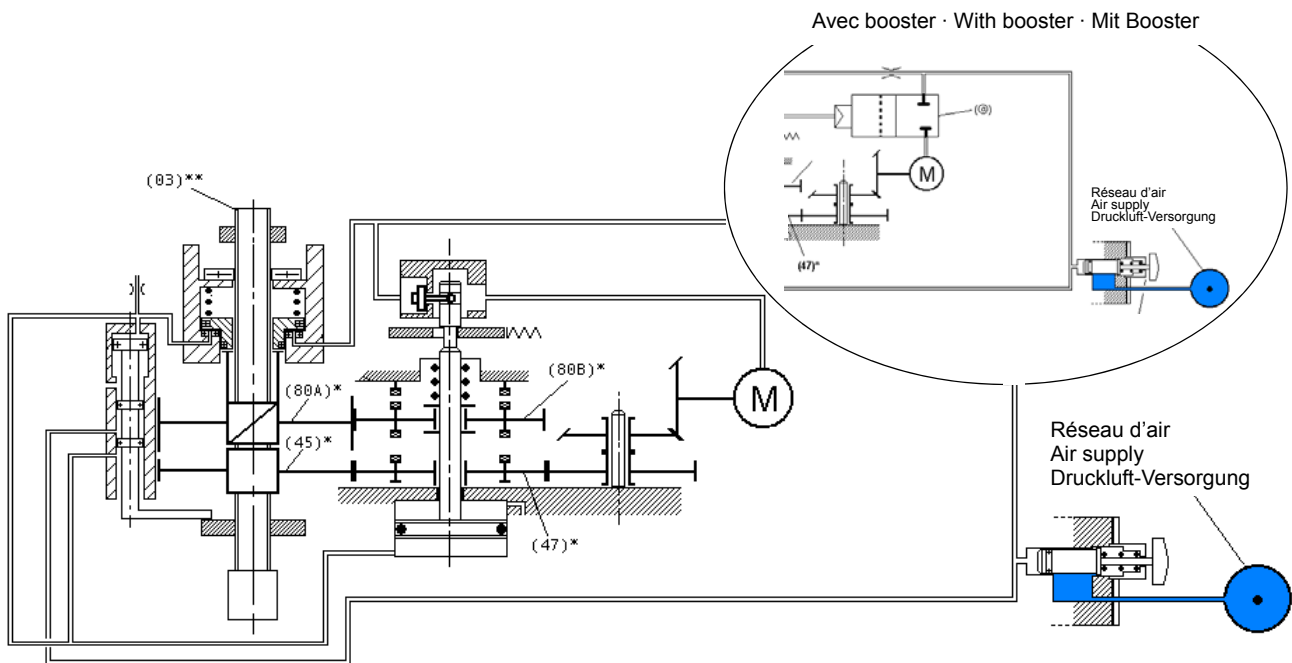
Machine à l'arrêt sous pression · Machine off under pressure · Maschine aus und unter druck
